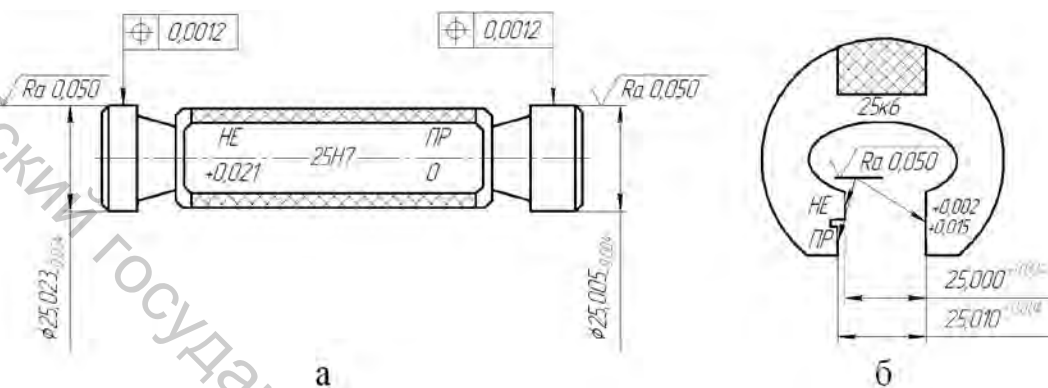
Размеры, шероховатость и маркировка:
